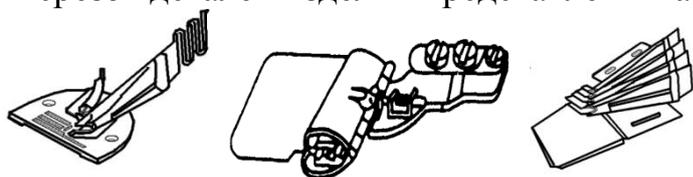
Спецприспособления для сборки прорезных карманов
